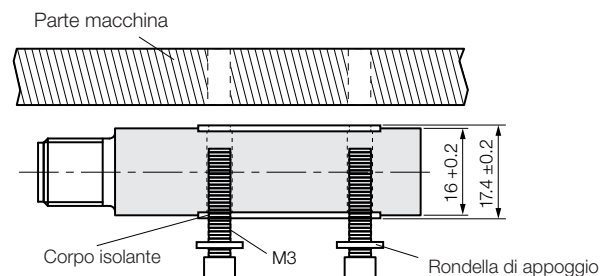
Montaggio della testa sensore con corpo isolante
